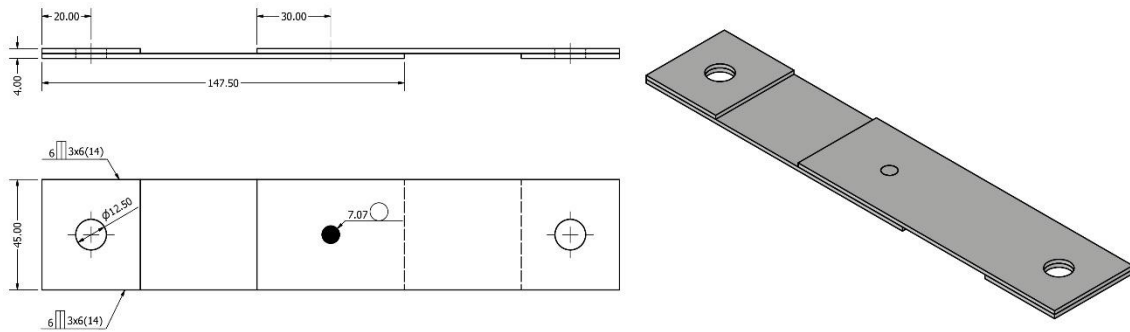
Dimensiones de las probetas formadas por dos chapas unidas por un punto de soldadura en mm
